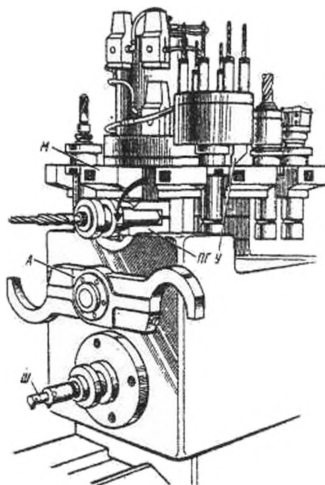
Загальний вигляд МАЗІ для окремих інструментів та багатошпіндельних головок:
